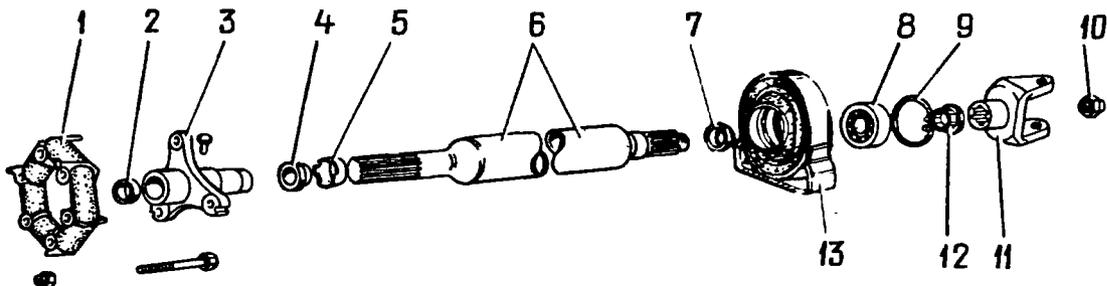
Детали переднего карданного вала: 1 - эластичная муфта; 2 - центрирующая втулка; 3 - фланец эластичной муфты; 4 - сальник; 5 - обойма сальника; 6 - карданный вал; 7 - пылеотражатель; 8 - подшипник; 9 - стопорное кольцо; 10 - гайка; 11 - вилка карданного шарнира; 12 - пылеотражатель; 13 - упругая опора
